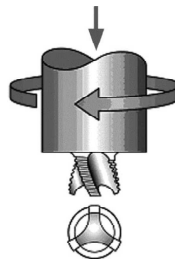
Outil « Flare-Triflute » développé par The Welding Institute (TWI), UK [Thomas et al. 03].
